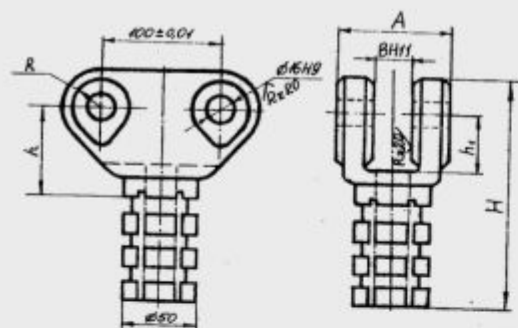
Сборные рубильники сборочных приспособлений: а – рубильник со сменными законцовками, б – рубильники со сменными рабочими поверхностями
